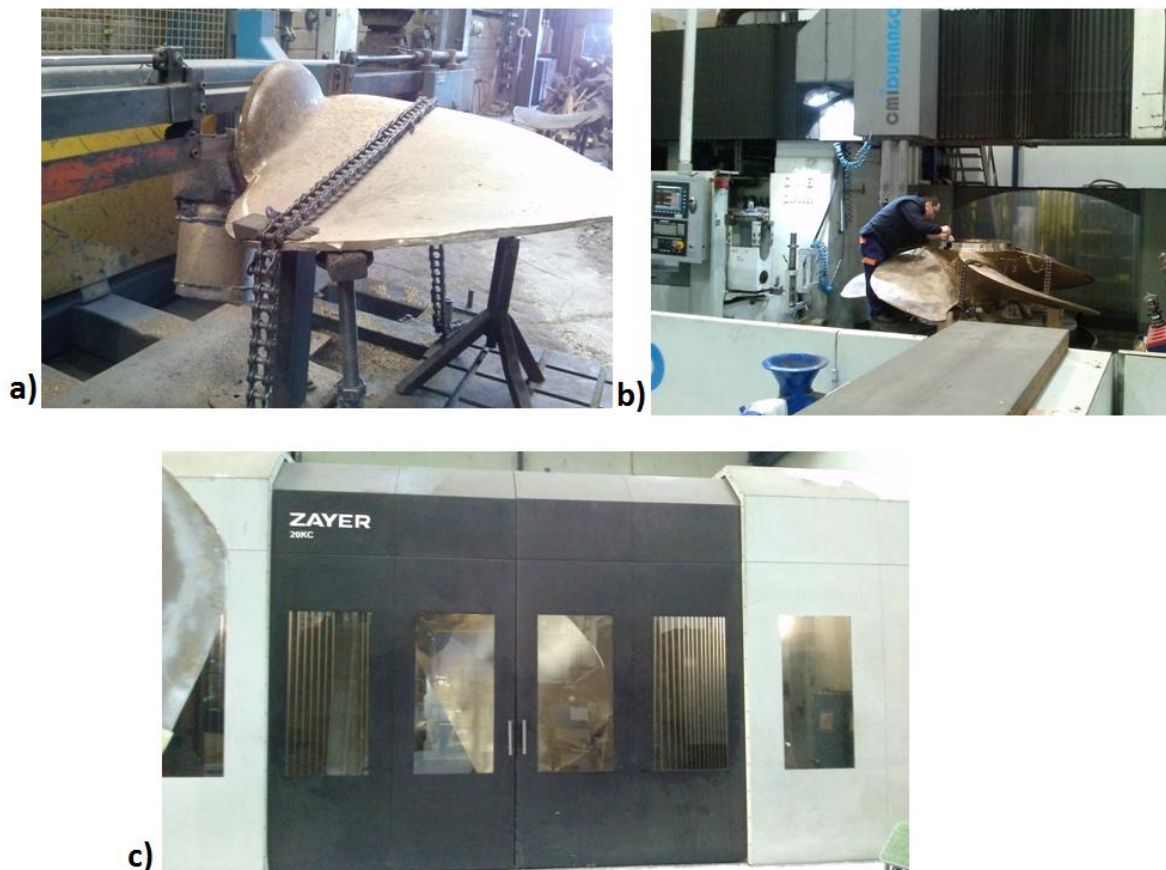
Maquinagem da peça fundida: a) corte e remoção do alimentador; b) maquinagem em torno CNC de hélice de passo fixo; c) maquinagem de uma pá de hélice de passo variável em fresadora CNC.
